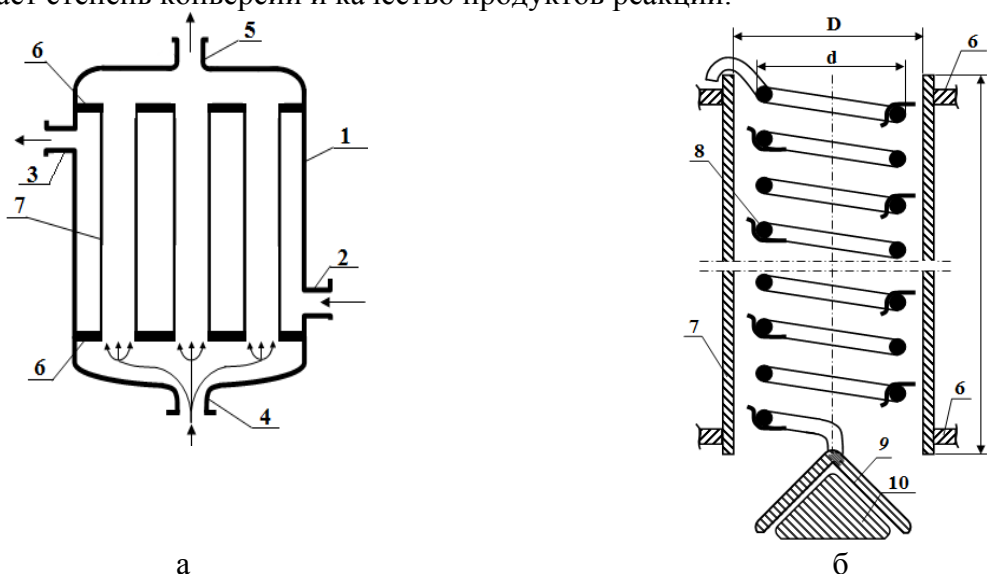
Кожухотрубный реактор. а – общий вид кожухотрубного реактора в разрезе, б – одна труба с цилиндрической пружиной, коническим пустотелым конусом, грузом и лопатками на витках цилиндрической пружины
